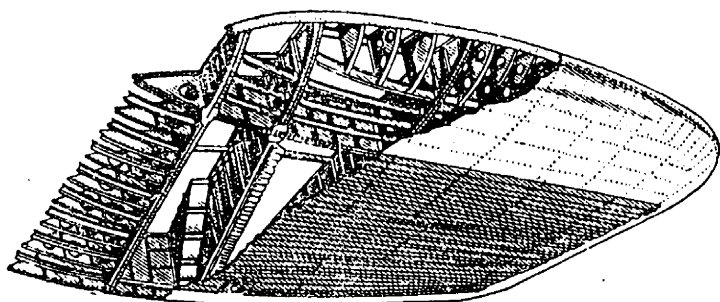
Short „Calcutta“. Клетка килевой балки поплавка.
